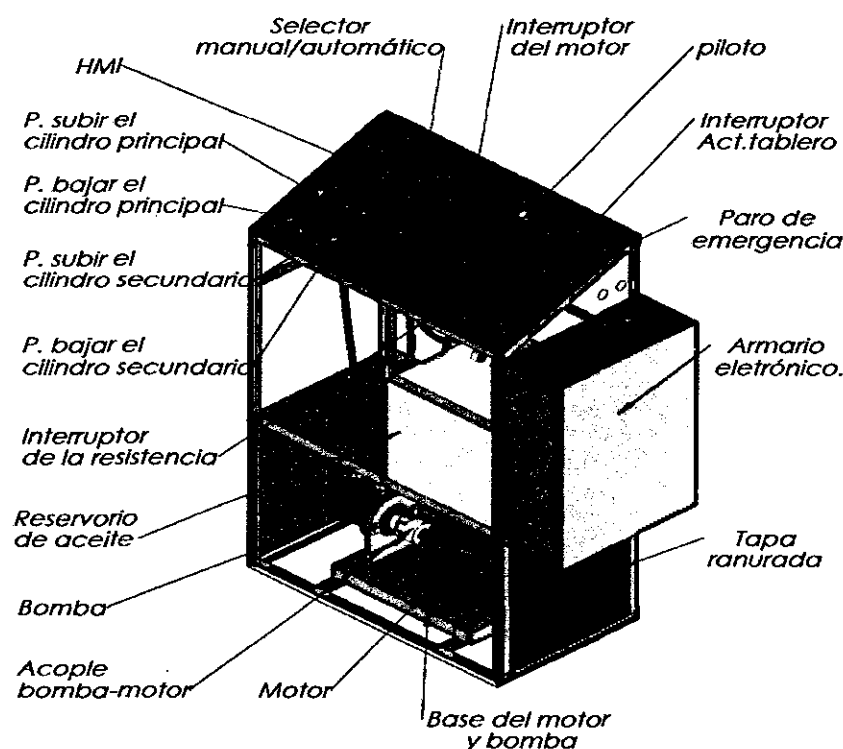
Componentes de la caja de control, diseñado en Solidworks.
